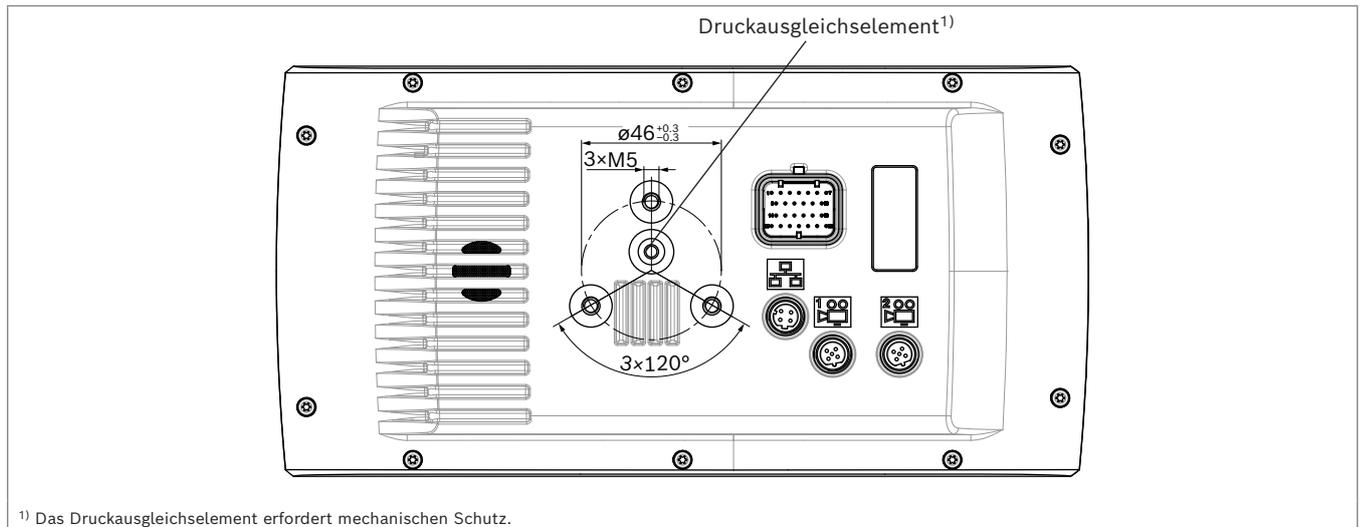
Ausschnitt für Einbau eines DI4 in ein Armaturenbrett
